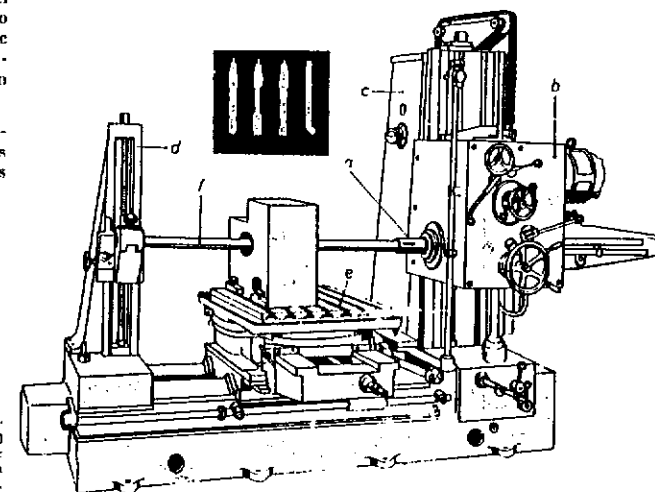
,2. Máquina horizontal de taladrar: a) husillo portatool; b) carro; c) columna de la máquina; d) columna auxiliar; e) mesa de la máquina; f) barra o eje de taladrar.
